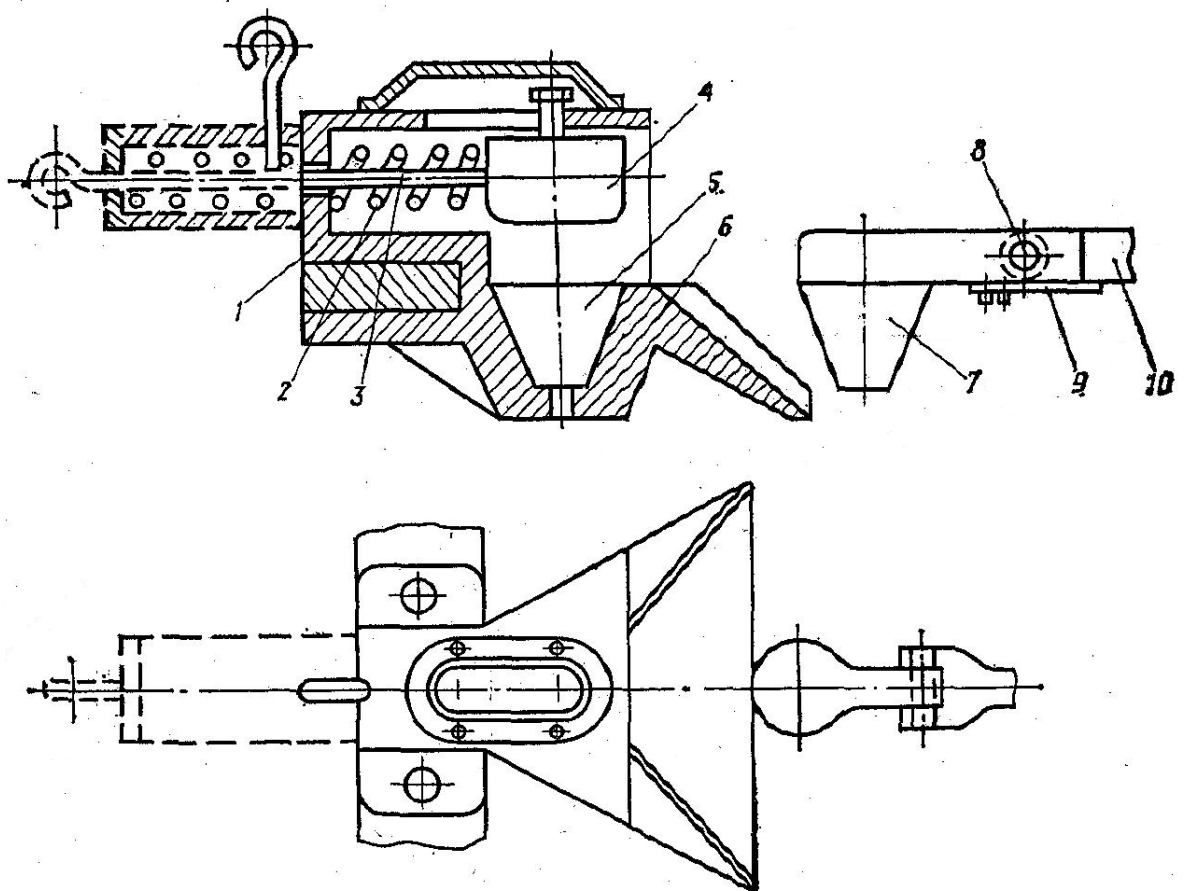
Конструкція автоматичного тягово-причіпного пристрою для тракторів класу понад 3: 1 – корпус; 2 – пружина; 3 – вісь; 4 – упор; 5 – заглиблення для ; 4 – спрямівник; 7 – виступ; 8 – шарнір; 9 – пластинчаста пружина; 10 – сниця (дишло)
